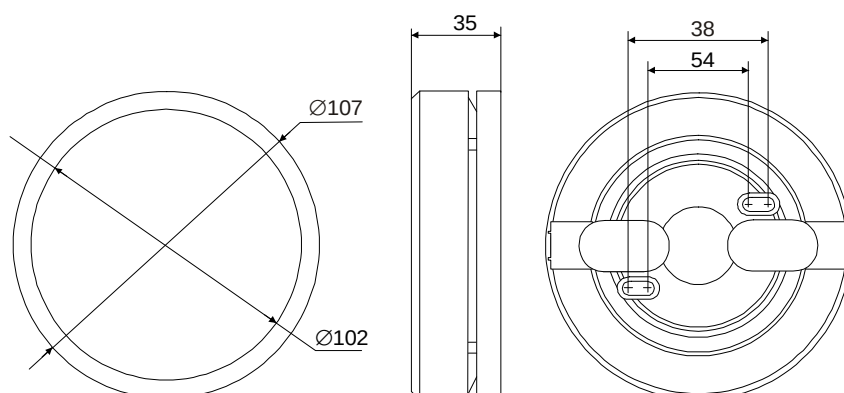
Габаритные размеры и расположение крепежных отверстий оповещателей DBS1224BW и DBS1224FW.
